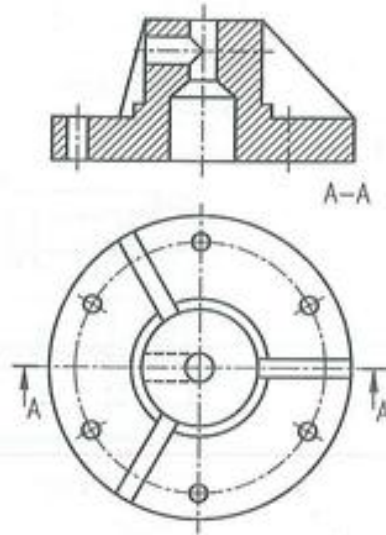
Ejemplo donde no pueden abatirse elementos al plano de corte.
